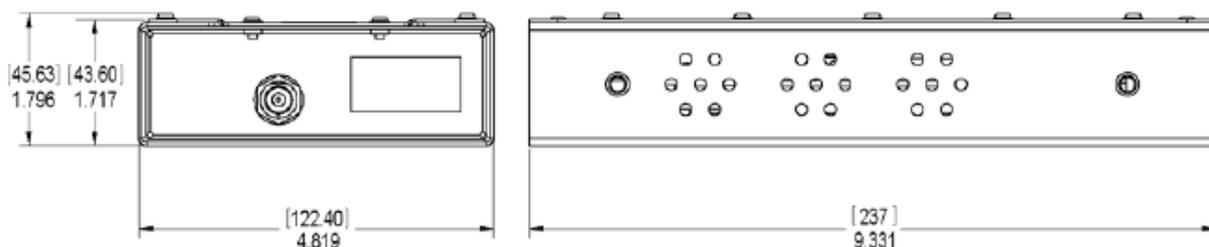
Изолированный цифровой преобразователь 7600, размеры
